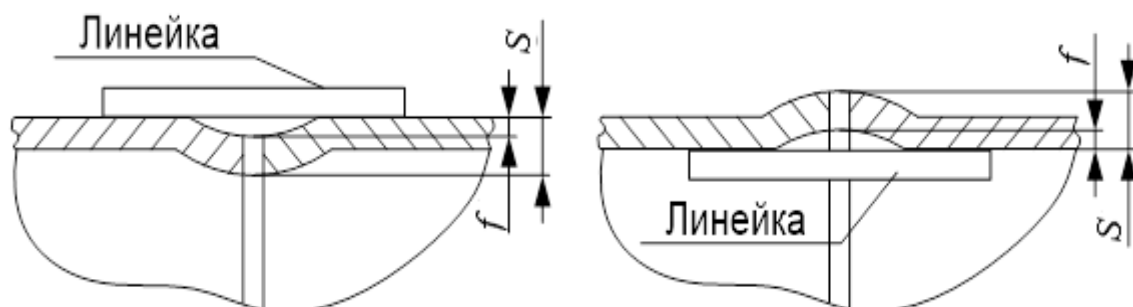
Контроль увода кромок продольных и кольцевых сварных соединений
